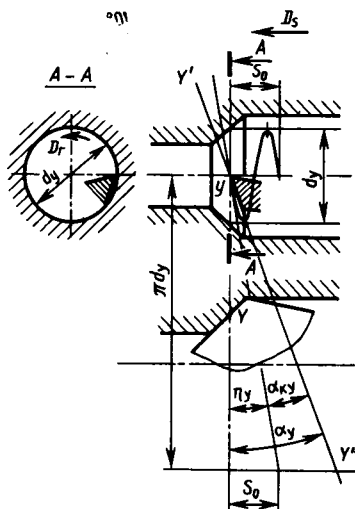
Траектория движения режущей кромки при обработке отверстия
